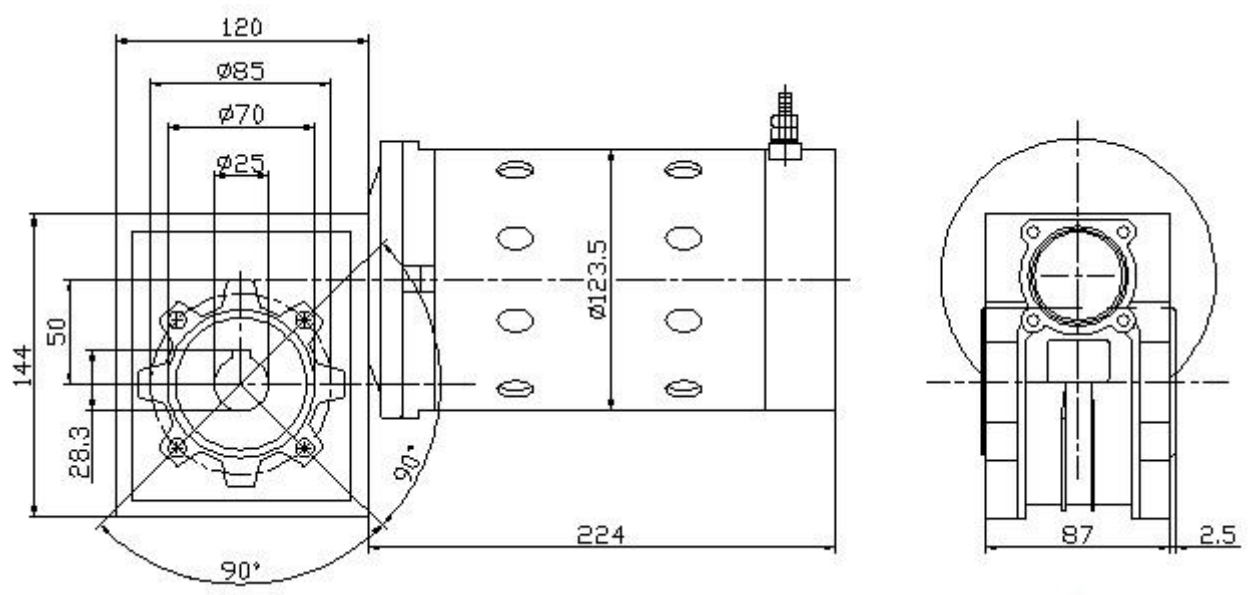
Габаритные и присоединительные размеры WG1188
